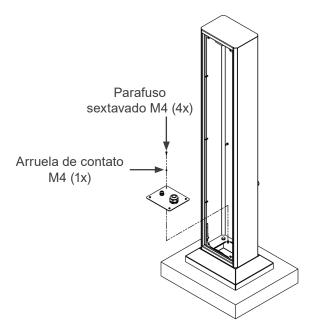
Ponto de aterramento da flange do totem WEMOB
